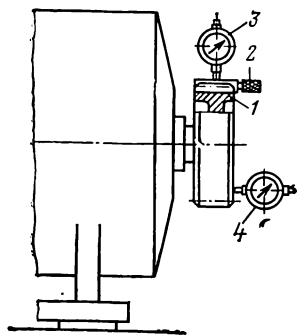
Проверка торцевого и радиального биения шестерни, надетой на конец вала электродвигателя
